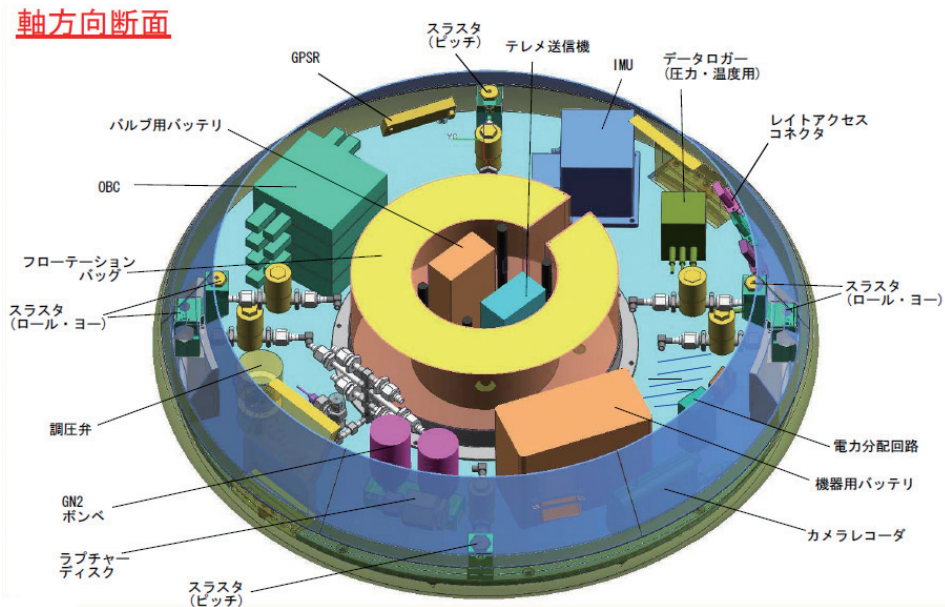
μ -LRS 機器配置図 (軸方向断面図示)
